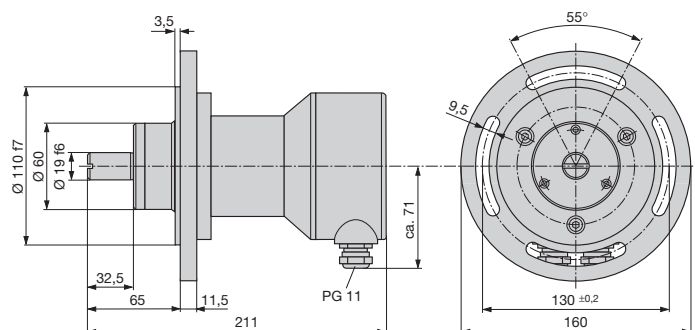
KINAX WT 707 mit Zusatzgetriebe, Schraubklemmen sowie Stopfbuchsen und Flansch.
